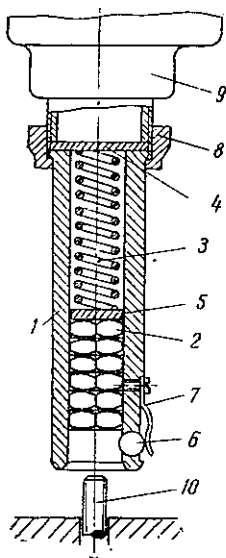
Cheie tubulară cu depozit de piulițe
